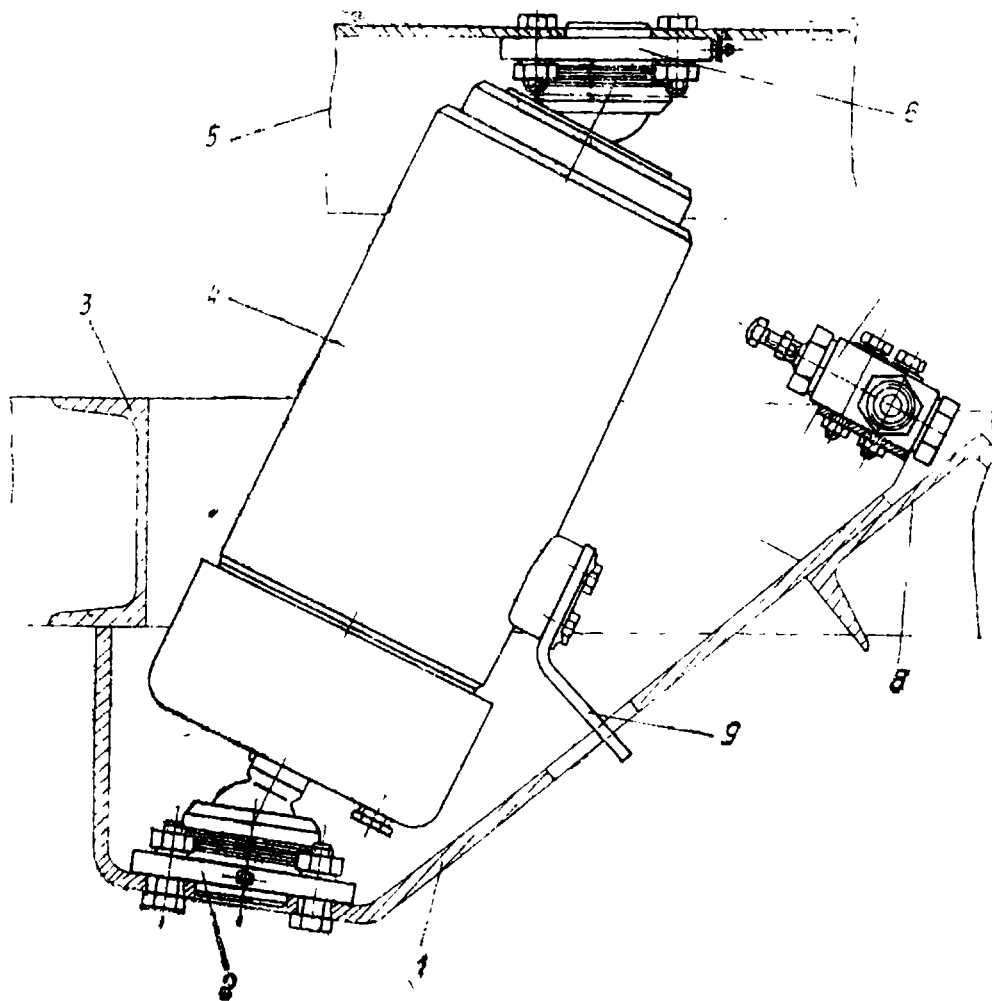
Крепление гидроцилиндра и ограничительного клапана:
